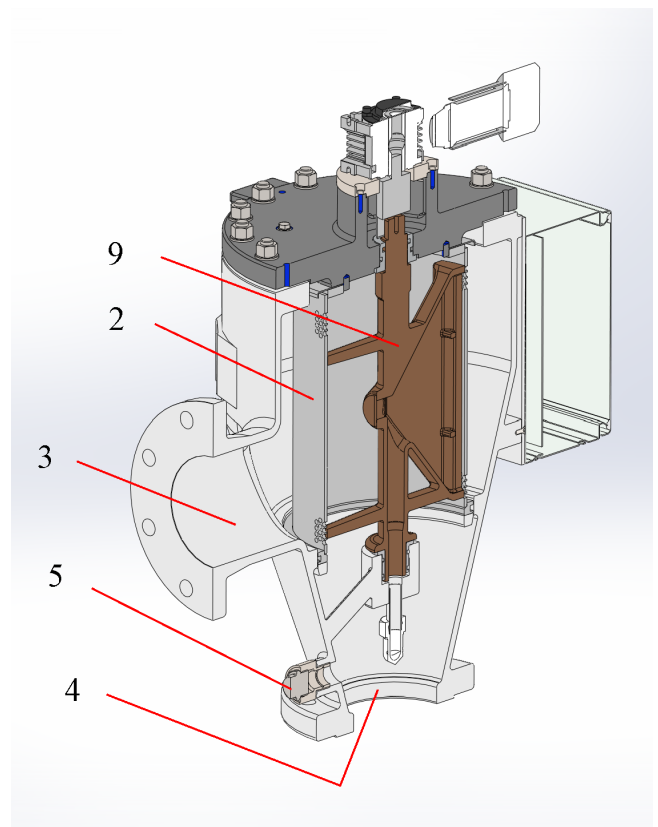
Bezeichnung der Hauptkomponenten R8-80
